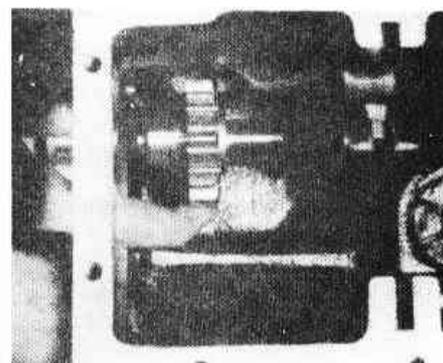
Блок шестерен промежуточного вала коробки передач типа В (Разд.7)
